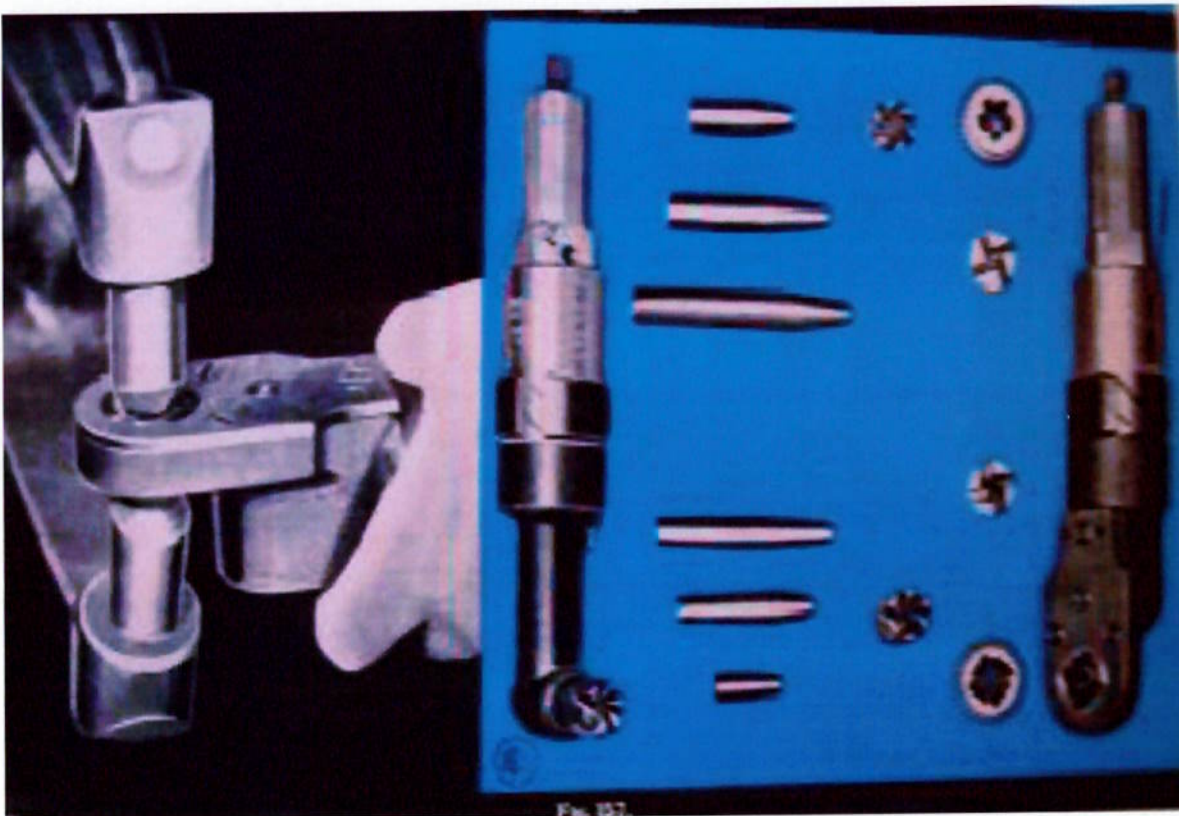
Fresador para ajuste da ponta do eletrodo [28].
